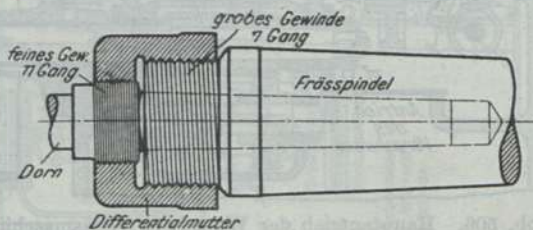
Einspannen des Fräasers mit einer Unterschiedsgewindemutter.
